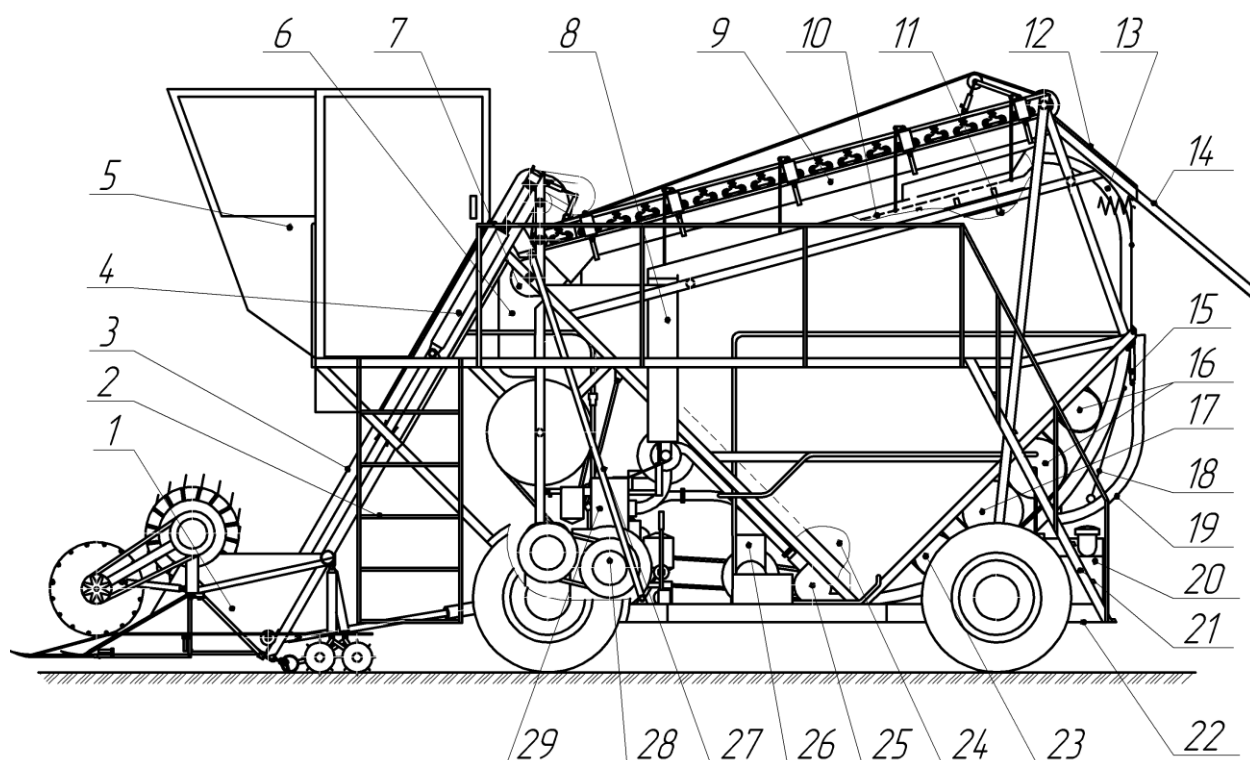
Схема зерноуборочного комбайна, вид справа: 1 – жатка; 2 – трап; 3 – наклонный транспортёр; 4 – гидроцилиндр управления наклонным транспортёром; 5 – кабина; 6 – закрытая передача; 7 – верхний диаметральный вентилятор; 8 – боковой лоток; 9 – устройство выделения зёрен из колосьев; 10 – нижнее решето; 11 – разравнивающий транспортёр; 12 – задний лоток; 13 – труба возврата; 14 – наставка; 15 – гидроцилиндр управления зернопроводом; 16 – гидропневмоаккумулятор; 17 – ресивер; 18 – гибкая штанга датчика; 19 – зернопровод; 20 – бак для хранения топлива; 21 – площадка с лестницей; 22 – рама; 23 – гидроаккумулятор; 24 – бункер; 25 – нижний диаметральный вентилятор; 26 – компрессор; 27 – кулиса; 28 – вариатор; 29 – двигатель
